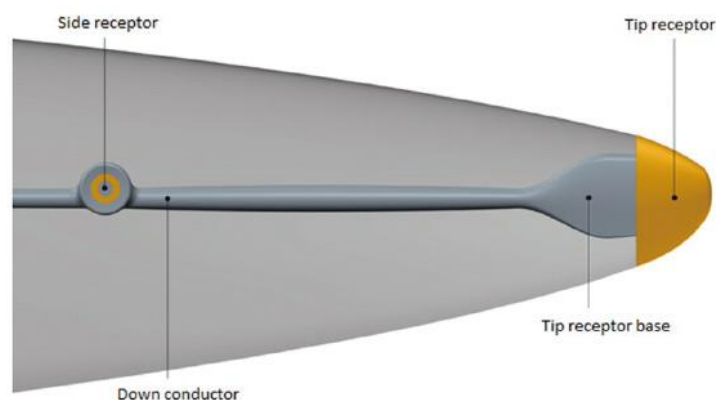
Captador del rayo en una pala genérica. Fuente: Blade Partners.
